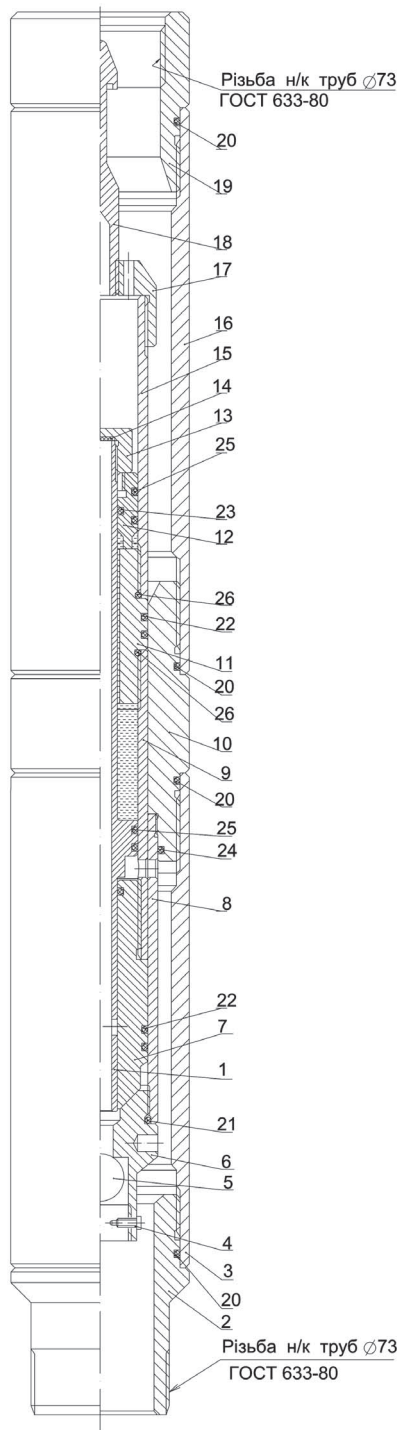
Глибинний пристрій для створення миттєвих депресій на пласт
